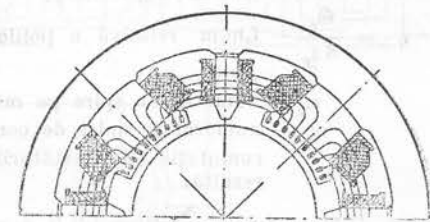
Mașină cu bobinaj de compensație (secțiune schematică).
